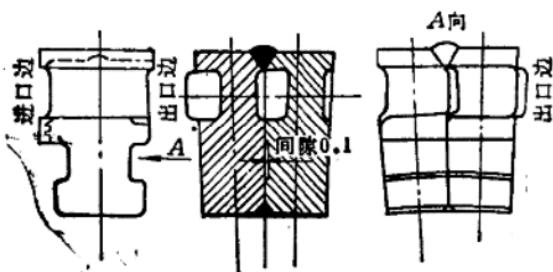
两片焊接成组的铣制调节级叶片结构
